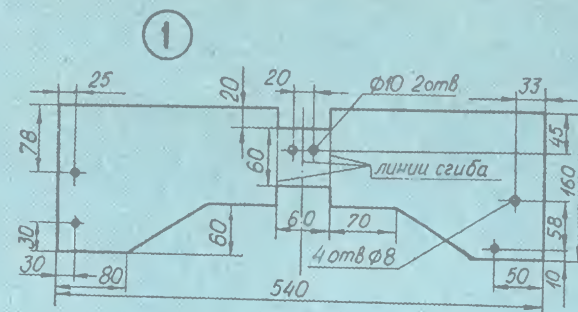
Эскиз заготовки кожуха для защиты переднего карданного шарнира.
